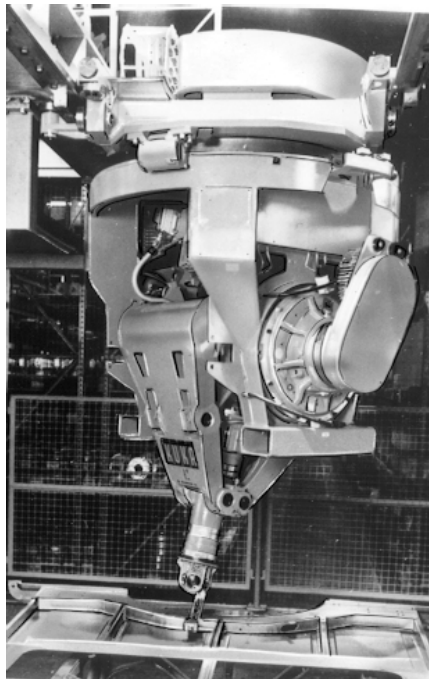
Сварочный робот фирмы КУКА.
